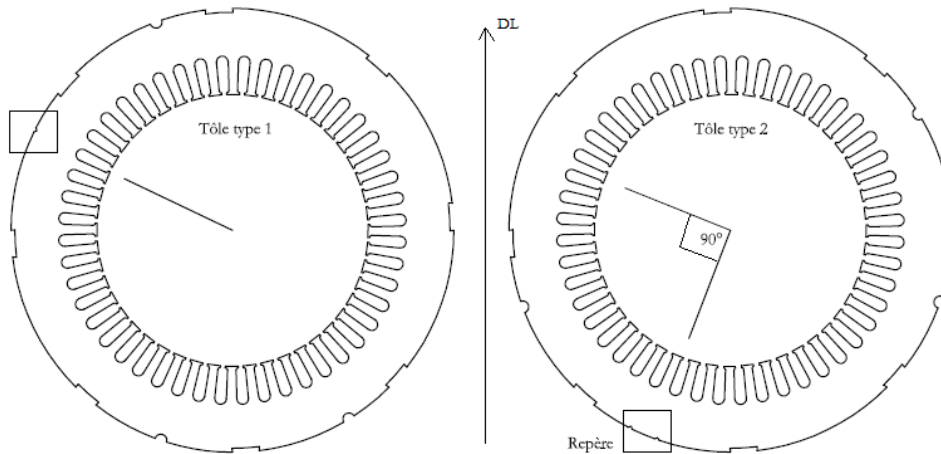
Plan de découpe de tôles décalées 90° sur la même plaque
